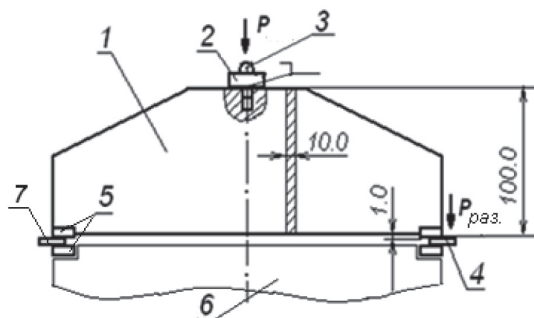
Схема нагружения пластин-резцов при испытании: 1 – пластина давяльная; 2 – пята опорная; 3 – шарик, диаметр 15 мм; 4 – пластина-резец из инструментального материала; 5 – пластина твердосплавная; 6 – нижняя плита пресса ДМ30; 7 – пластина для выравнивания; P – сила давления пресса на давяльную пластину; $P_{\text{раз}}$ – статическая нагрузка для разрушения пластины
